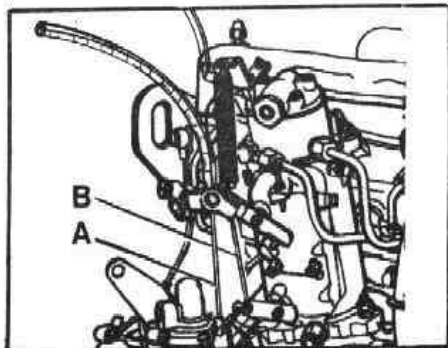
Desmontaje de los cables de acelerador y estrangulador
